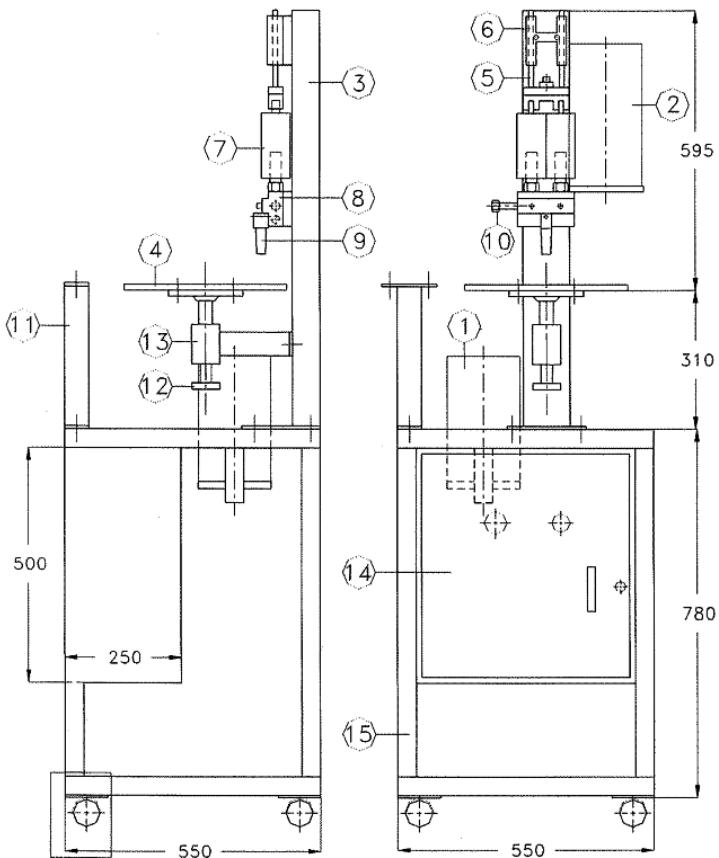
Dimensiones de la máquina y componentes mecánicos.
